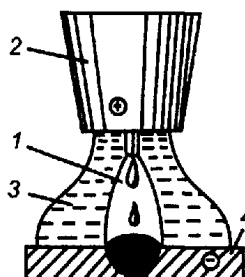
Схема механизированной сварки в защитных газах
